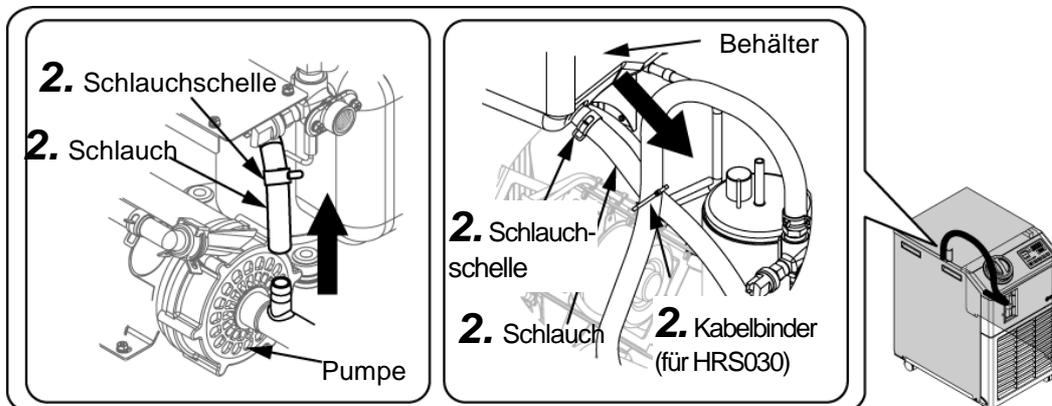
Entfernen des Schlauchs (zwischen Behälter und Pumpe)
